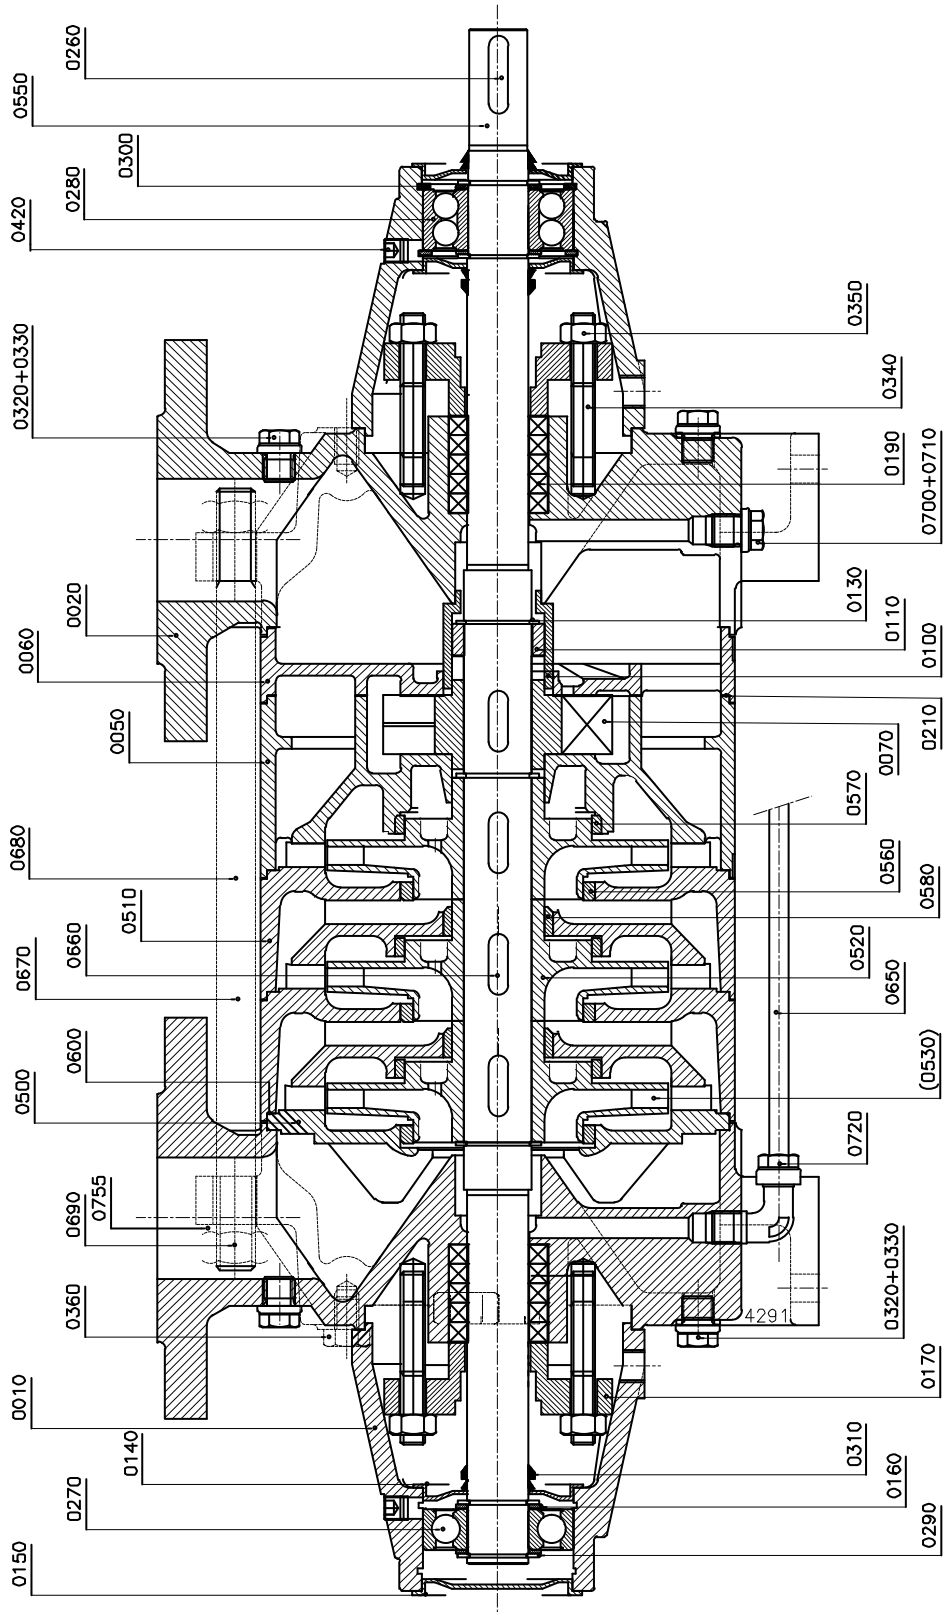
MCHZS 14a/b med tung lagerkonstruksjon.
